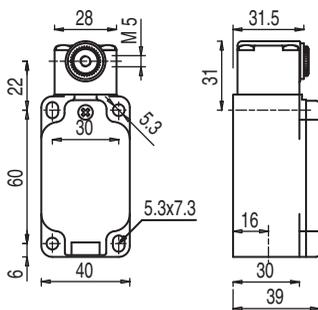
Dimensiones S300-P13C1-M20-CB y S300-P13C1-M12-CB en mm
